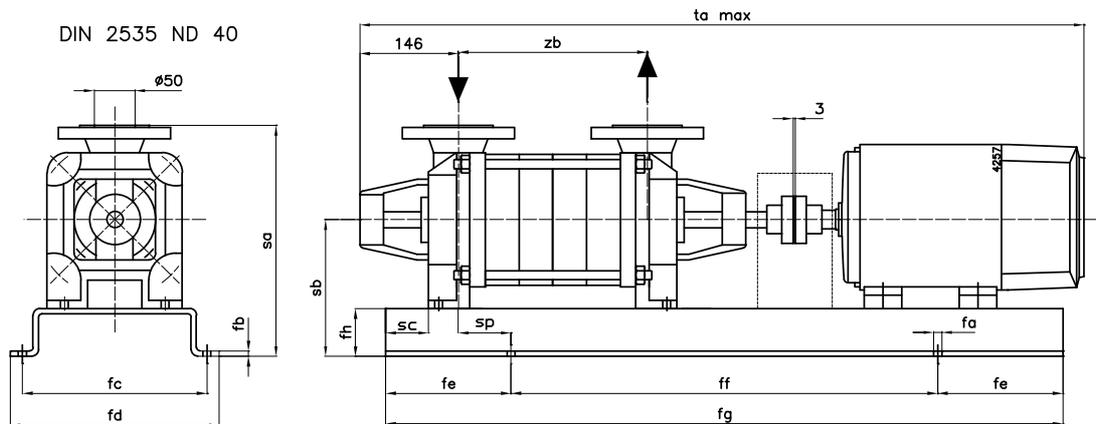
Габаритный чертеж агрегата MCHZ(S) 14b.
